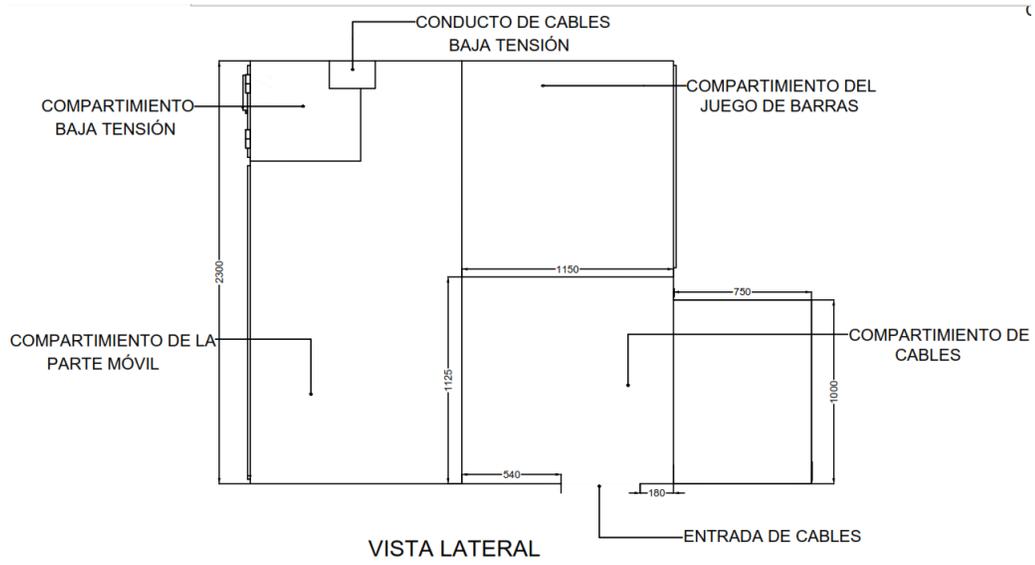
Plano mecánico de celda de conexión - vista lateral externa.
